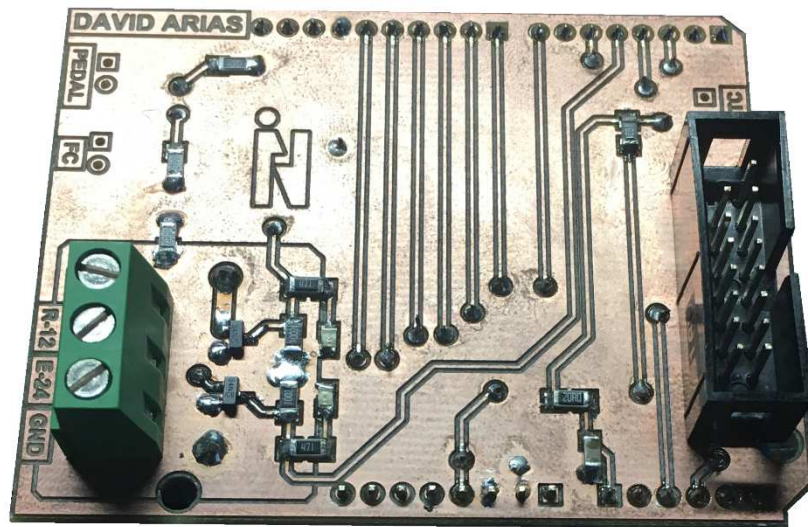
Foto de la placa de control tras soldar todos los componentes.
